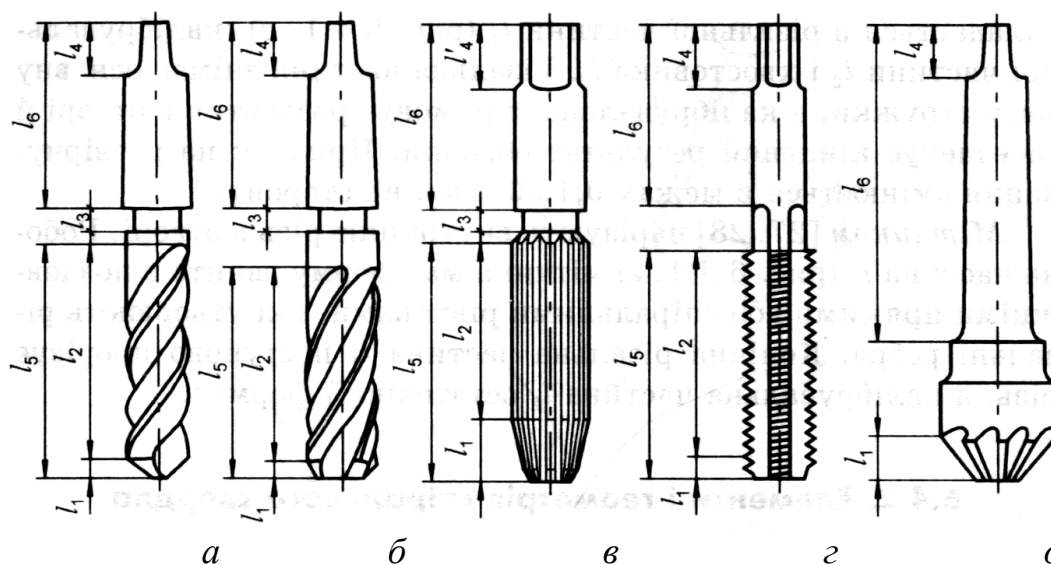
Різальні інструменти для обробки отворів: спіральне свердло (а); зенкер (б); розвертка (в); мітчик (г); зенківка (д); l - різальна частина; l_2, l_2' — напрямна та калібрувальна частини; l_3 — шийка; l_4 — лапка; l_5 — робоча частина; l_6 — хвостовик
